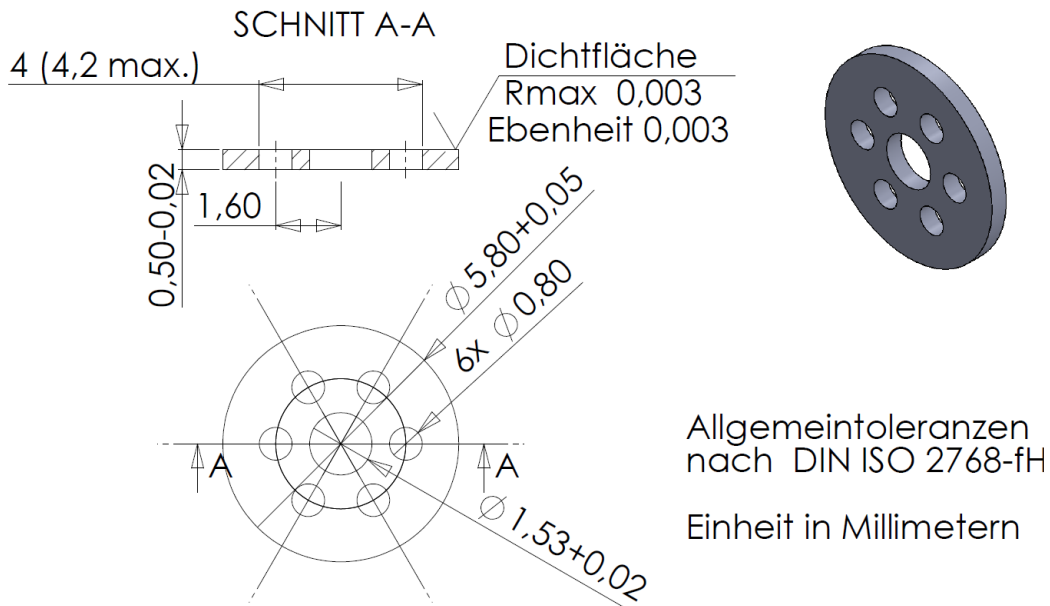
Technische Zeichnung einer Ventilscheibe zur Aufnahme eines Schirmventils der Firma miniValve.
